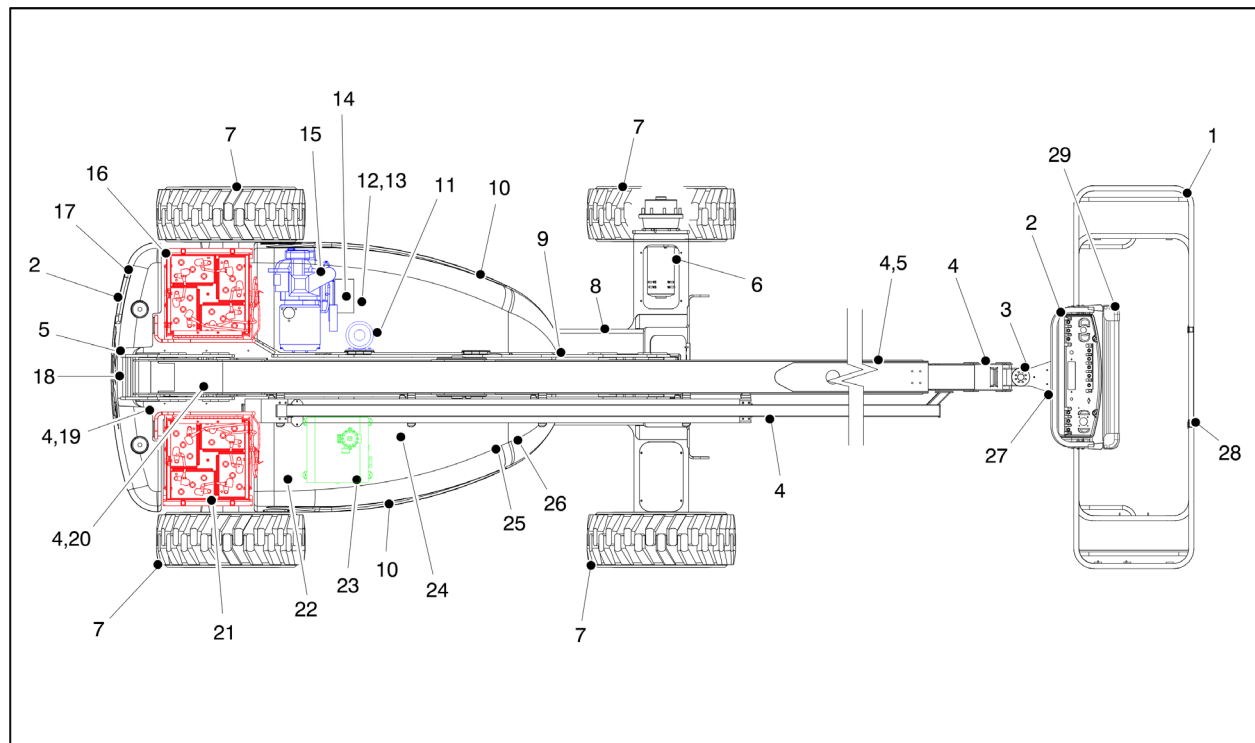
Základní nomenklatura – list 1 ze 3
